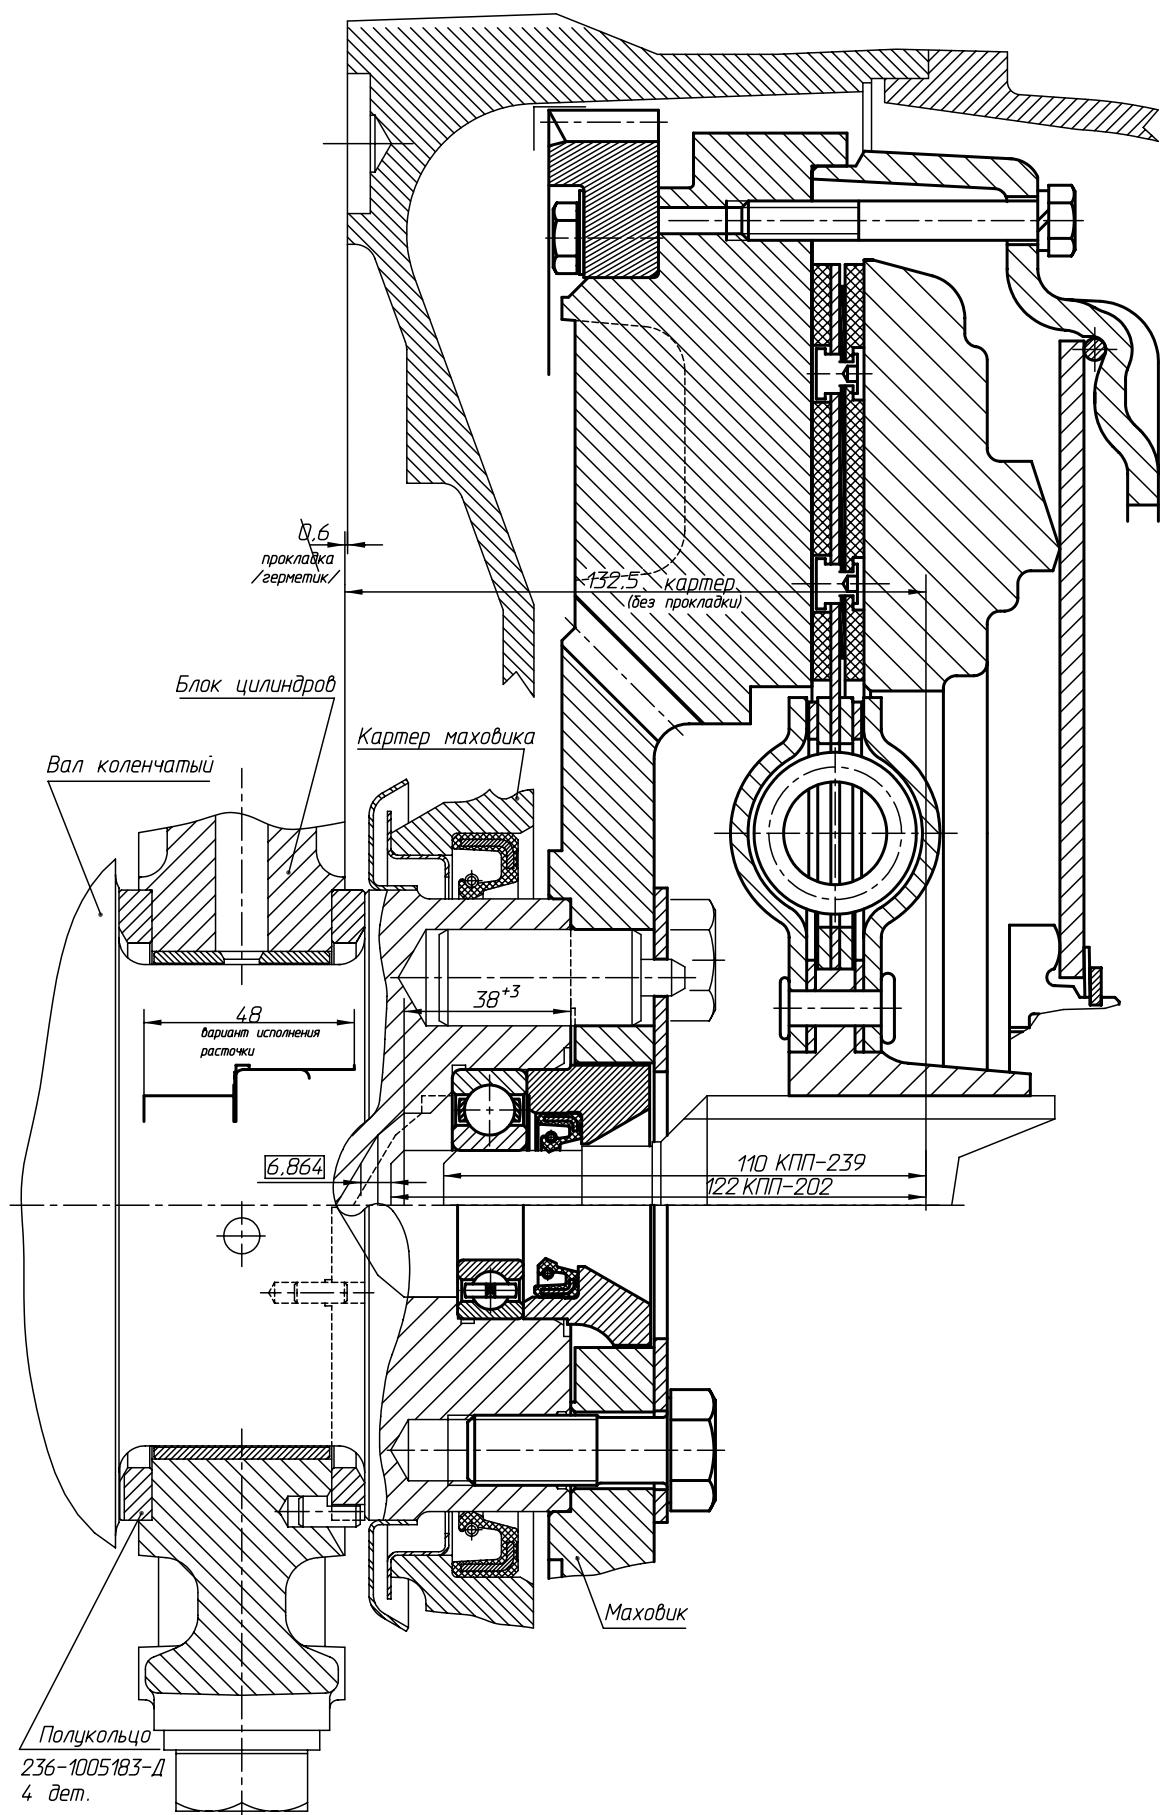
Установка маховика, сцепления и КП ЯМЗ-239 на двигатели типа ЯМЗ-7511 и ЯМЗ-7601
